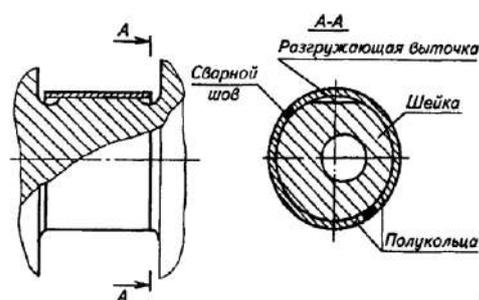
Схема восстановления шеек коленчатого вала двигателя ЗМЗ-53 приваркой стальных полуколец
